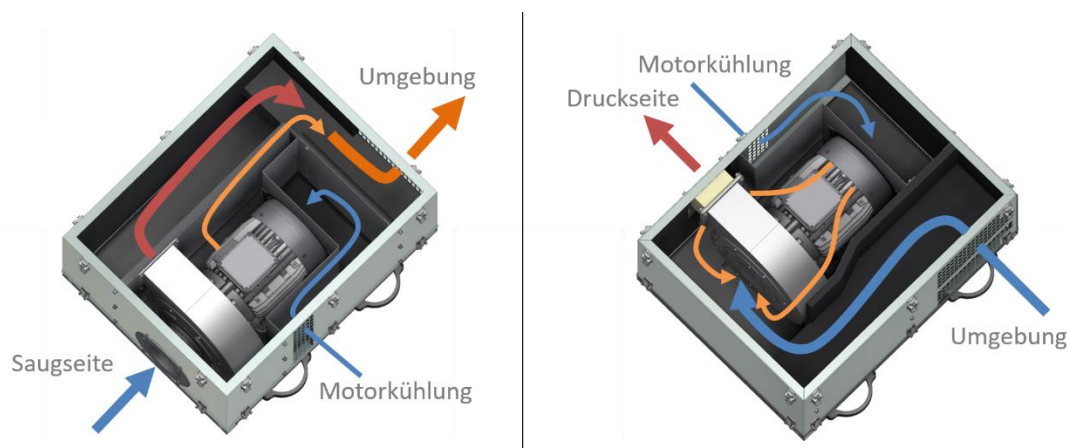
Schallschutzlösungen für schnell drehende Ventilatoren für saugseitige und druckseitige Anwendung
